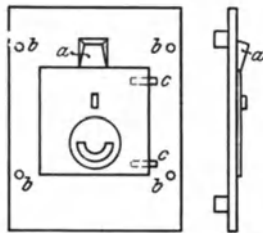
Frankenfelds Modellplatte, Rote Hütte 1827.
